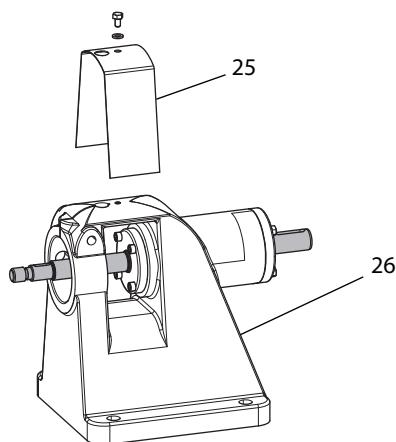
Extracción de la cubierta del apoyo del rodamiento
